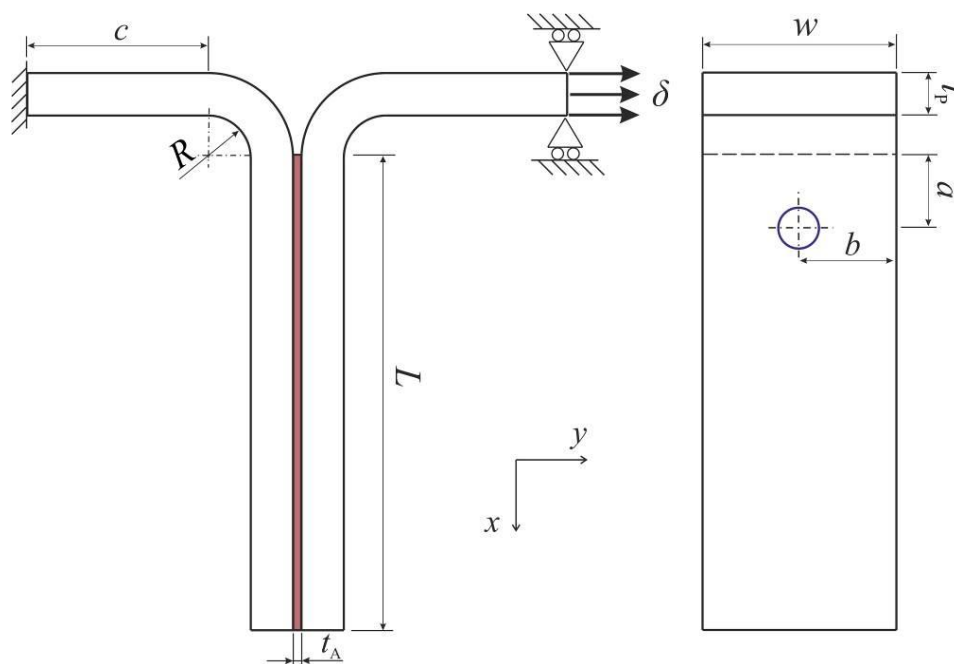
Dimensões e geometria das juntas T-peel [2].
